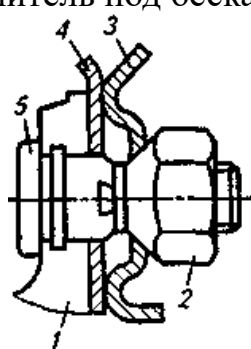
Крепление колеса легкового автомобиля: 1 — ступица; 2 — гайка; 3 — диск колеса; 4 — тормозной барабан; 5 — болт
